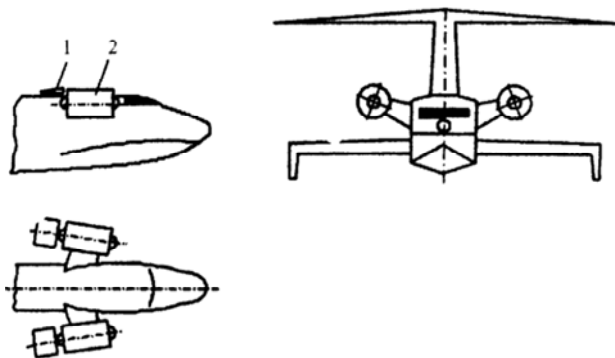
Схема установки носовых двигателей в корпусе:
